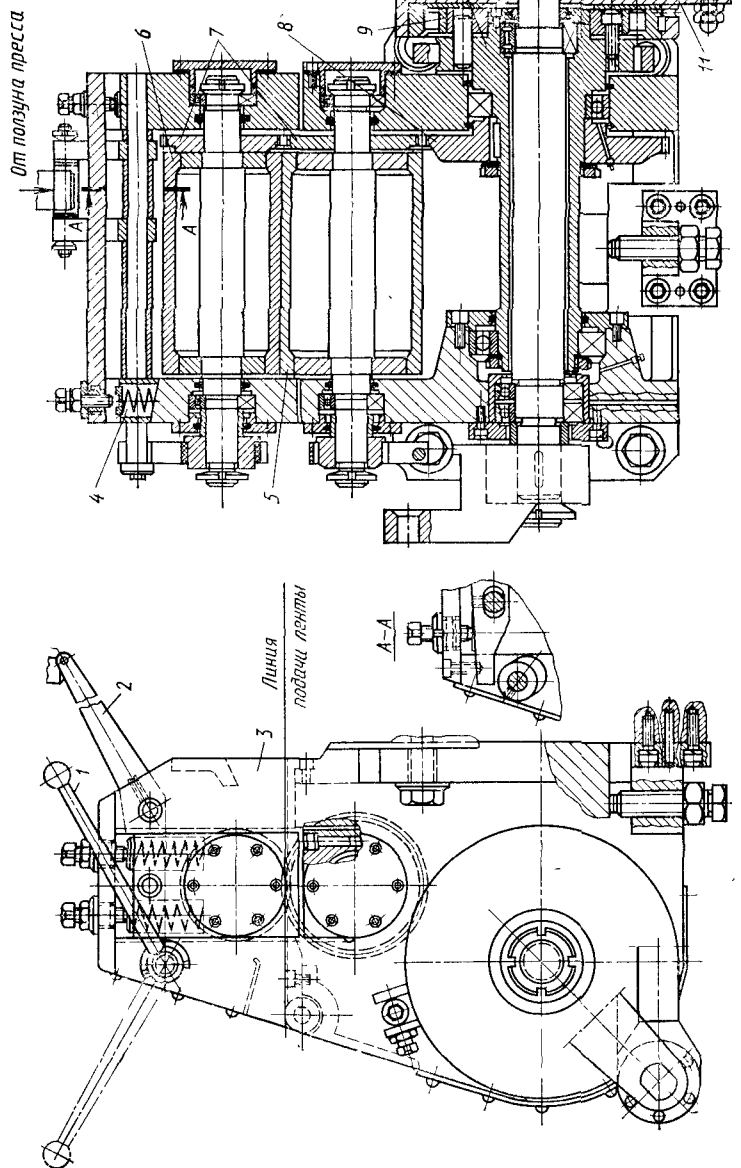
Конструкция подающей каретки валковой подачи для перемещения ленты
